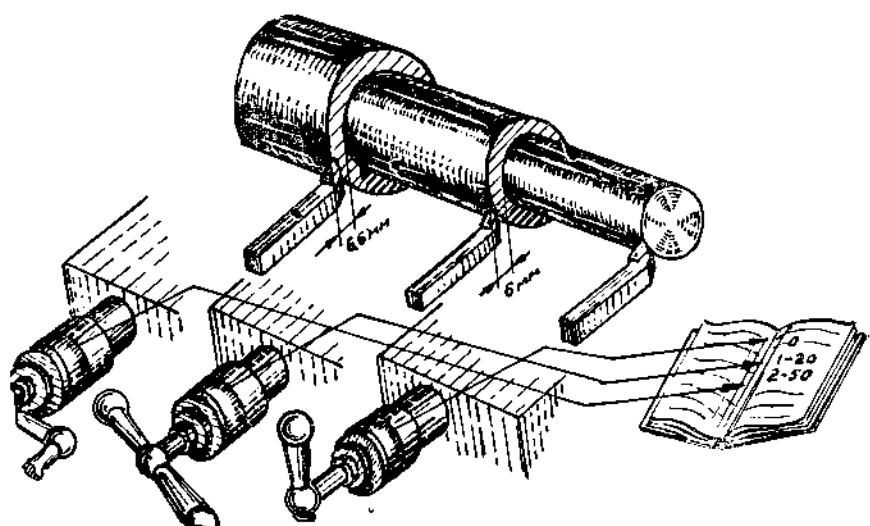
г. На таких деталях Борткевич применяет прямой порядок обхода детали резцом
